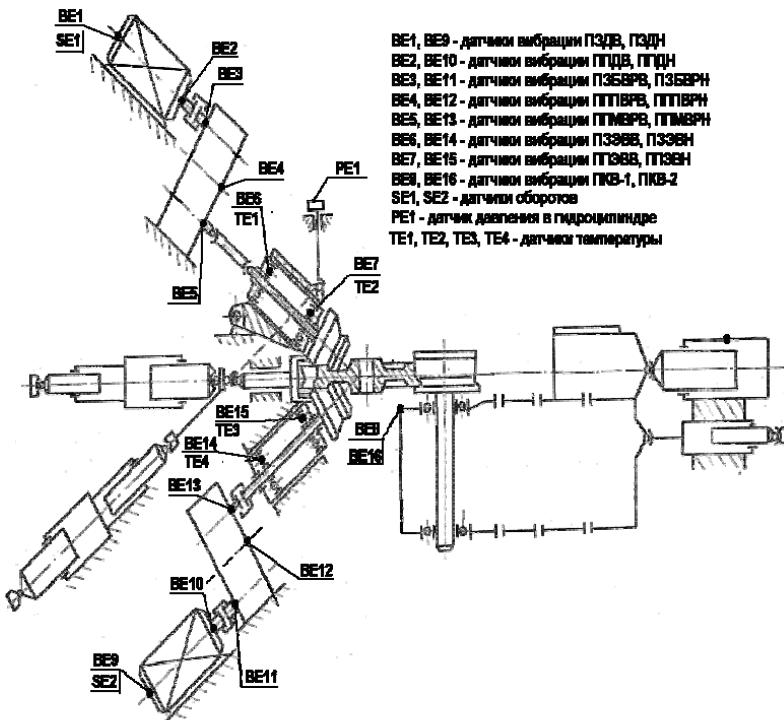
Конструкция колесо-прокатного стана и места установки датчиков вибрации
